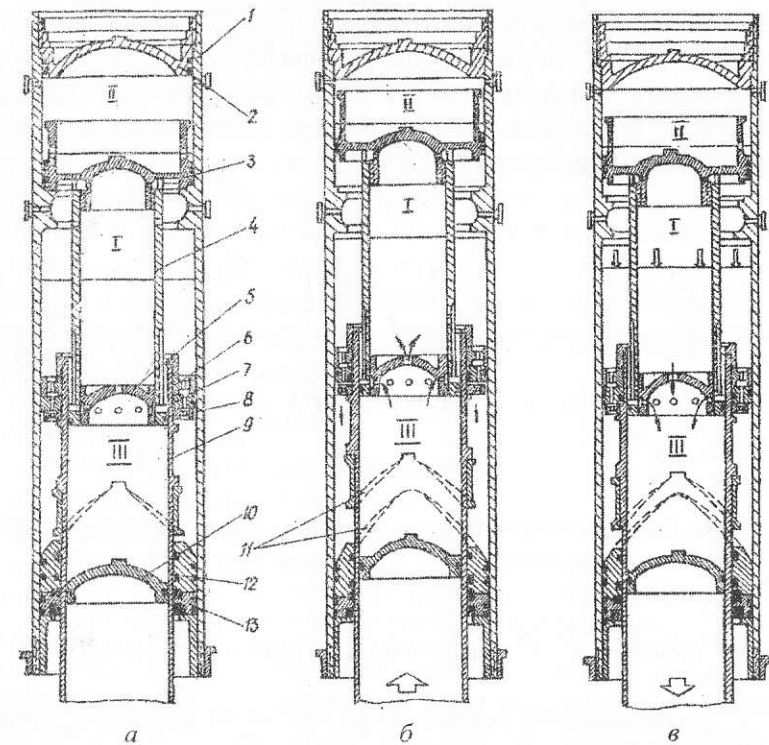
Амортизатор двокамерний із «плаваючою» трубою дифузора, рідинно-газового типу, з гальмуванням мастила на прямому і зворотному ході: а – амортизатор не обтиснутий; б – прямий хід штока; в – зворотний хід штока; 1 – циліндр; 2 – верхнє денце; 3 – плаваючий поршень; 4 – труба дифузора; 5 – дифузор; 6, 7, 13 – букси; 8 – клапан; 9 – шток амортизатора; 10 – денце; 11 – сферичні кулачки; 12 – сальник
